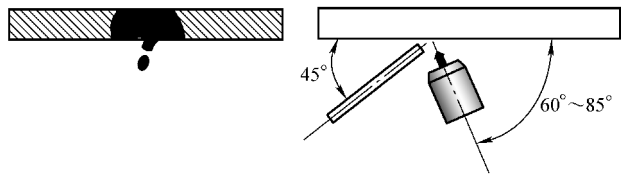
手工氩弧仰焊的焊枪与填丝
